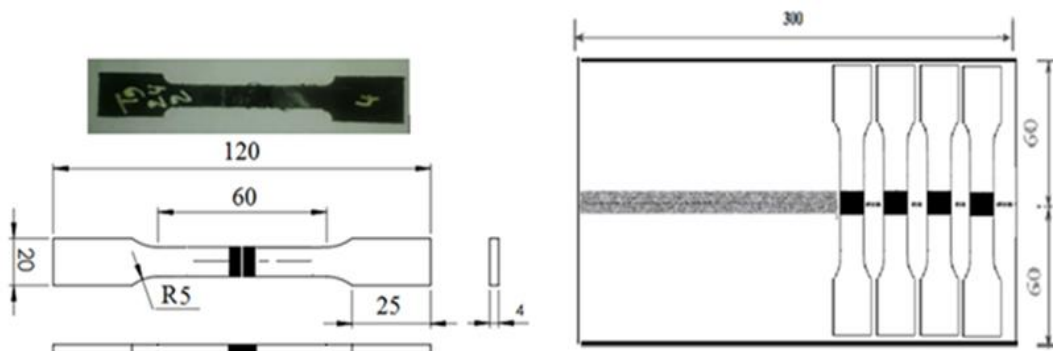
Géométries des éprouvettes de traction après Soudage FSW.
